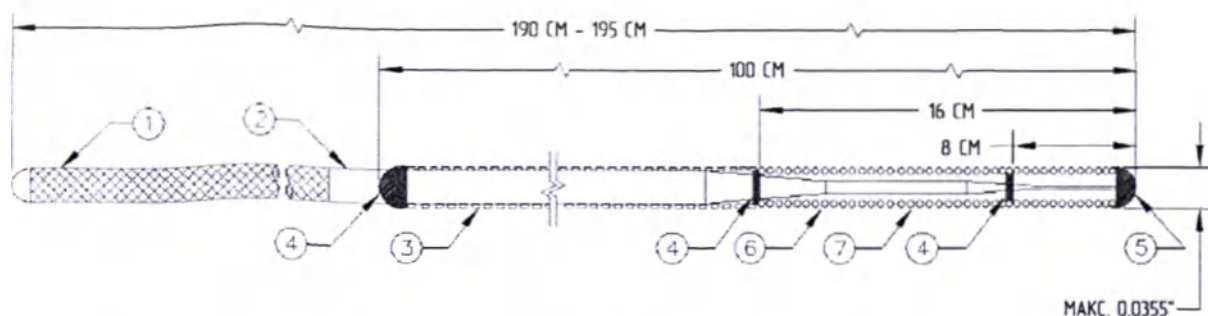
HI-TORQUE SUPRA CORE 35 (190 см, тип кончика - прямой)
